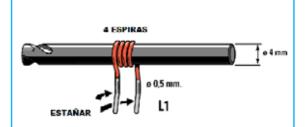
Para realizar la bobina L1 hay que envolver 4 espiras juntas utilizando cable de cobre esmaltado de 0,5 mm de diámetro sobre una broca de 4 mm. Hay que raspar los extremos para eliminar el barniz protector y posteriormente estañarlos.
